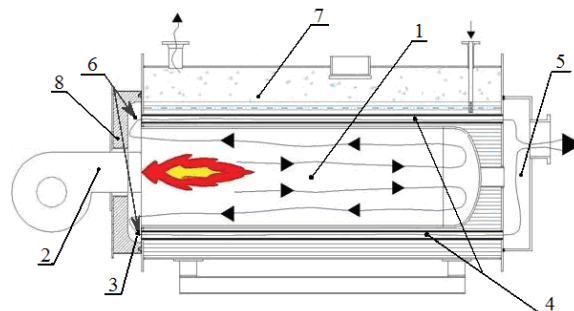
Конструктивная схема жаротрубного котла: 1 – жаровая топка; 2 – горелка; 3 – поворотная камера; 4 – конвективный пучок дымогарных труб; 5 – сборный дымовой короб; 6 – точки замера температуры (места установки терпар); 7 – водяной объем; 8 – крышка
